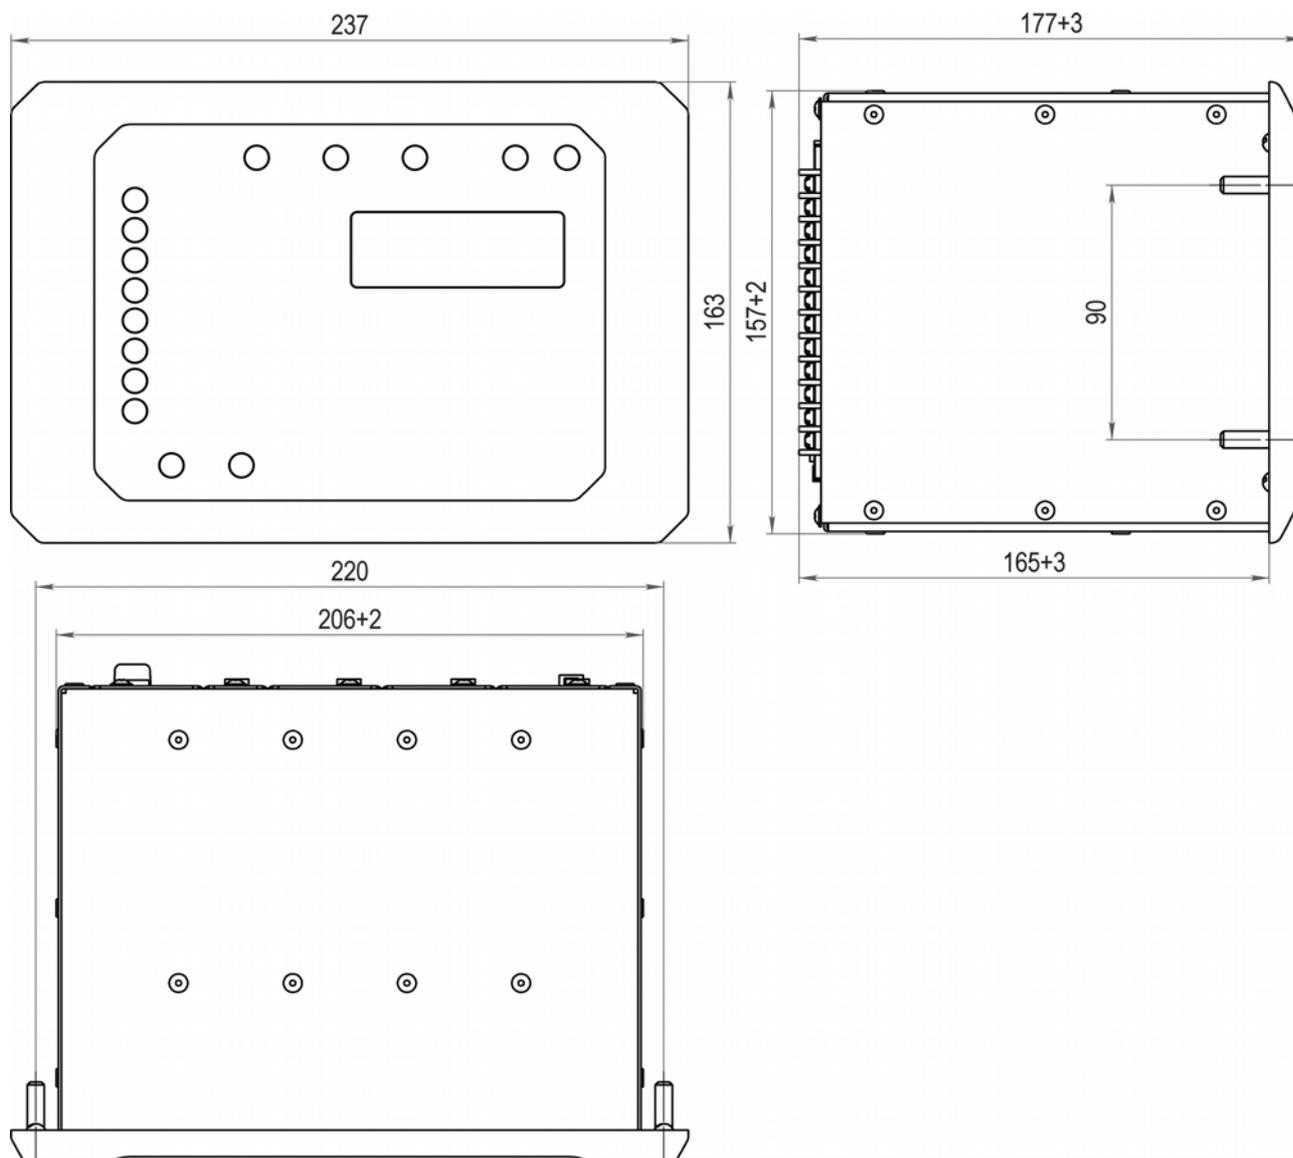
Габаритные размеры устройства УМПЗ/ТЭК.
